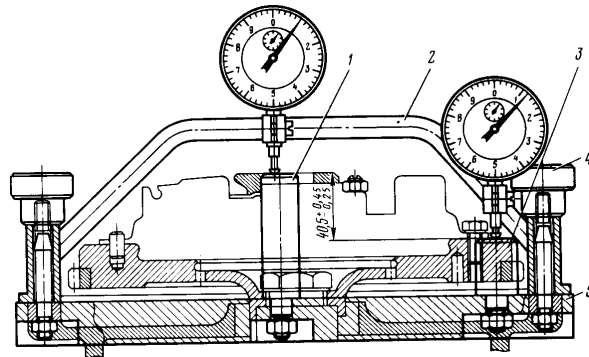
Приспособление для проверки биения торца маховика и для регулировки положения пяты рычагов сцепления: 1 — контрольная стойка пяты сцепления; 2 — перемычка с индикаторами; 3 - контрольная стойка торца маховика; 4 — зажимная гайка; 5 — установочная плита
